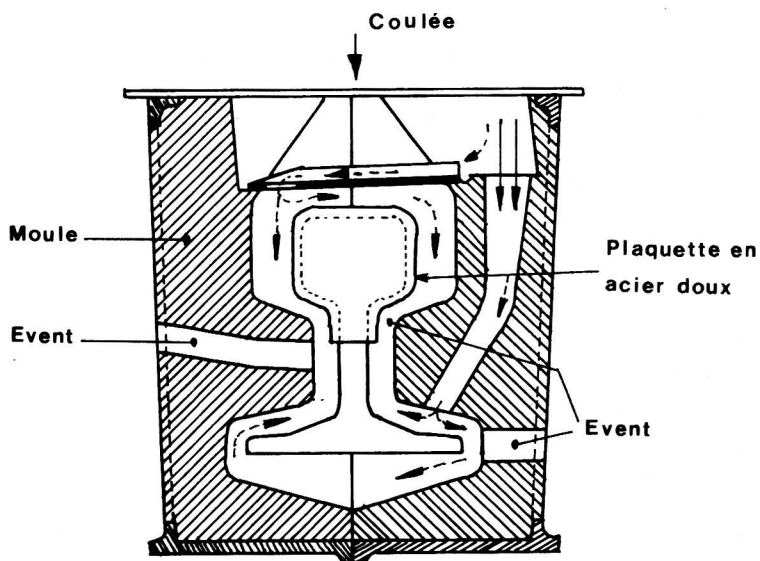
Schéma de principe de la soudure à plaquette
